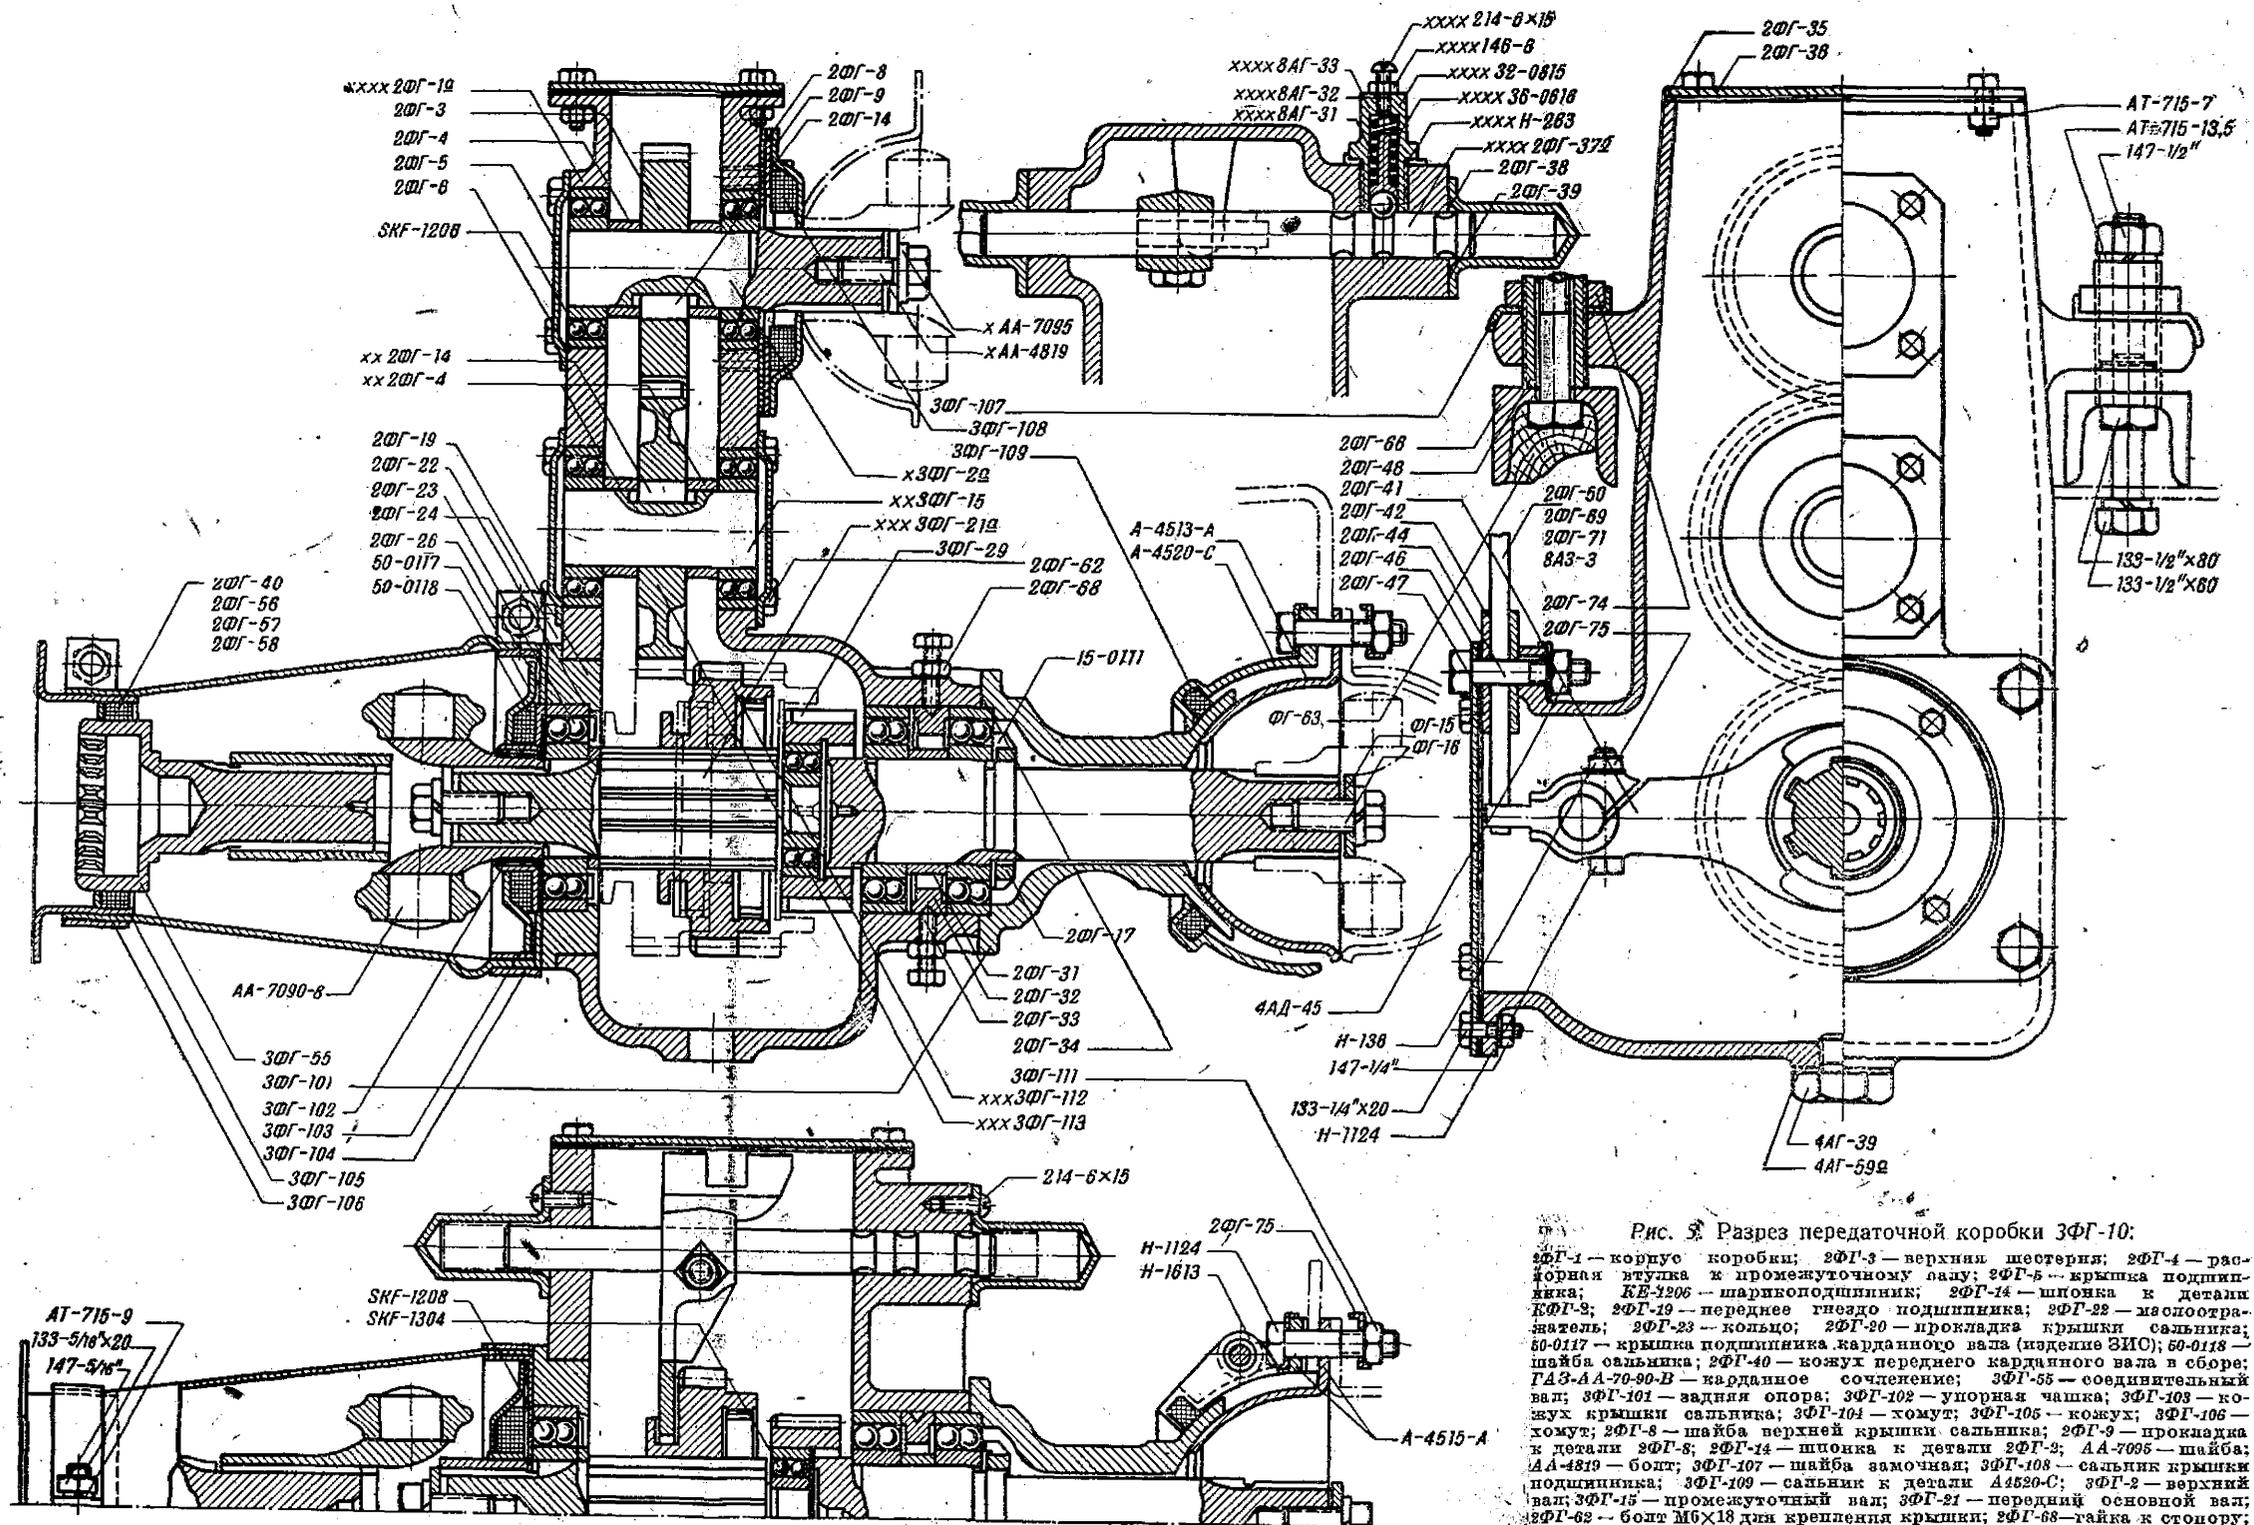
Разрез передаточной коробки 3ФГ-10.
